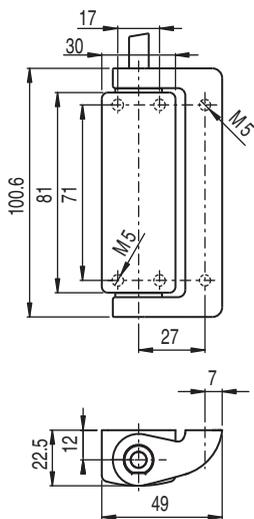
Dimensões do S400-M4CB2-T em mm
